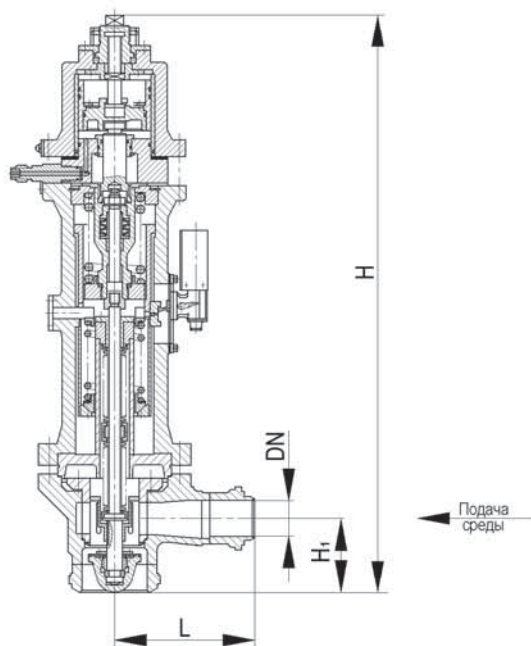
Клапанное бортовое запорное устройство
